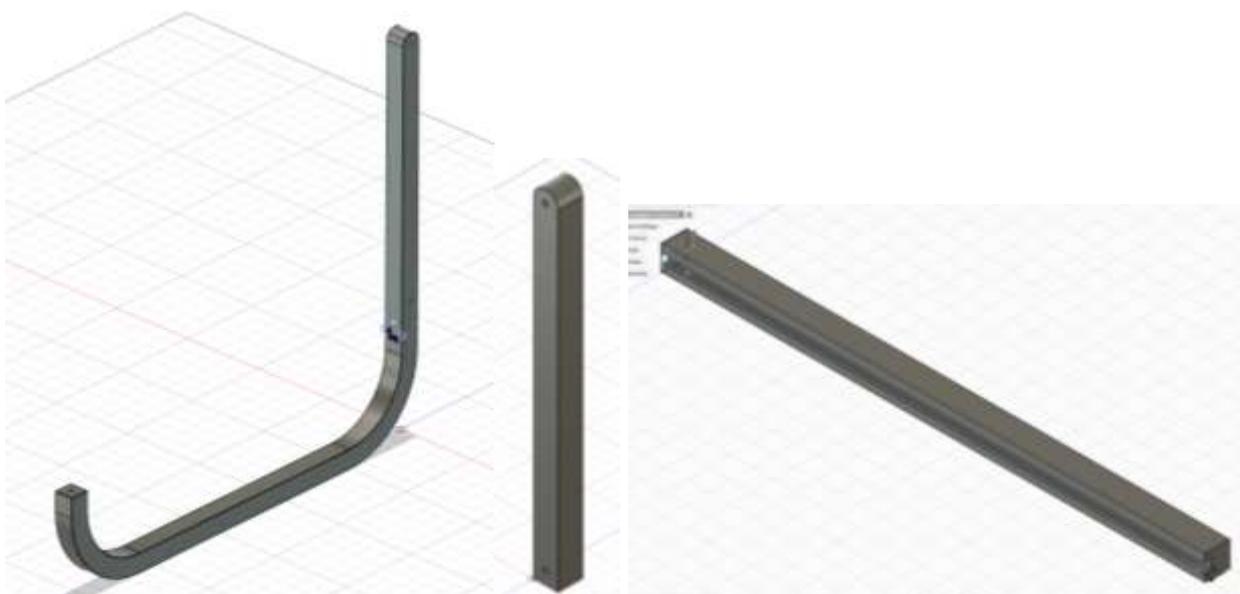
Модули корпуса, изготавливаемые из древесины бука
